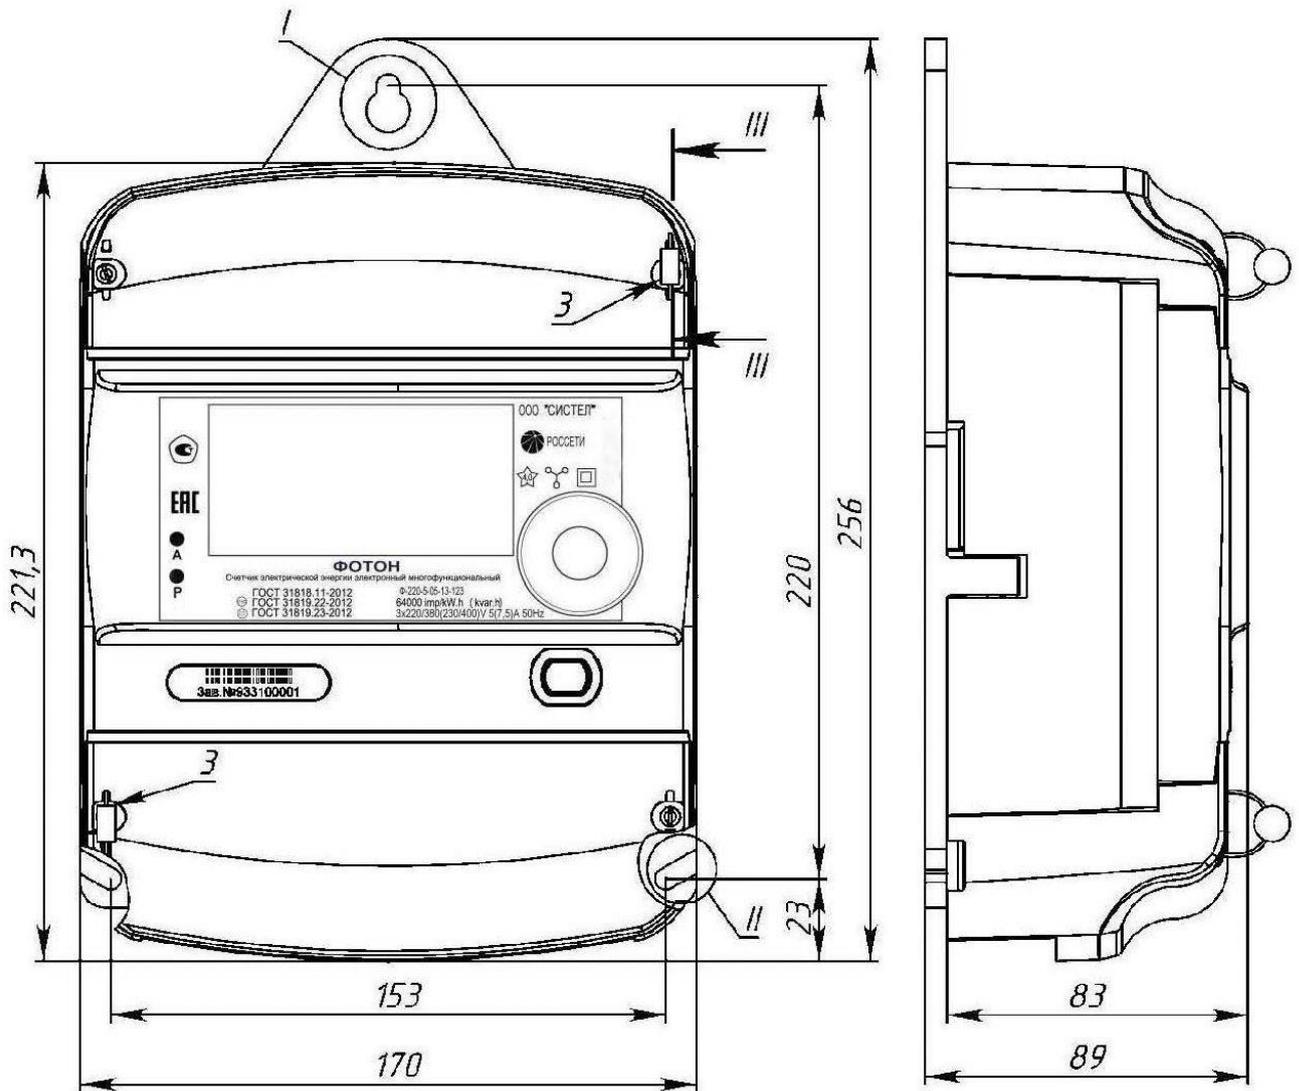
Внешний вид и габаритные размеры счетчика
